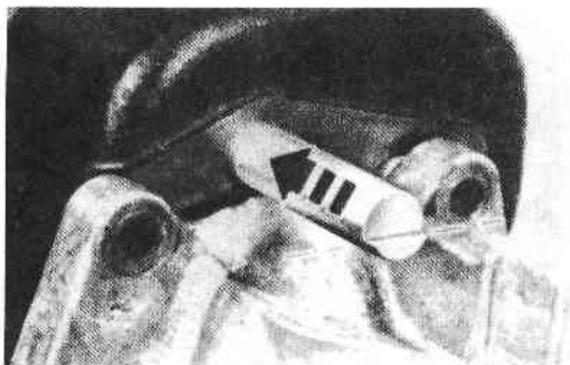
Установка промежуточного вала коробки передач типа В (Разд. 7)
